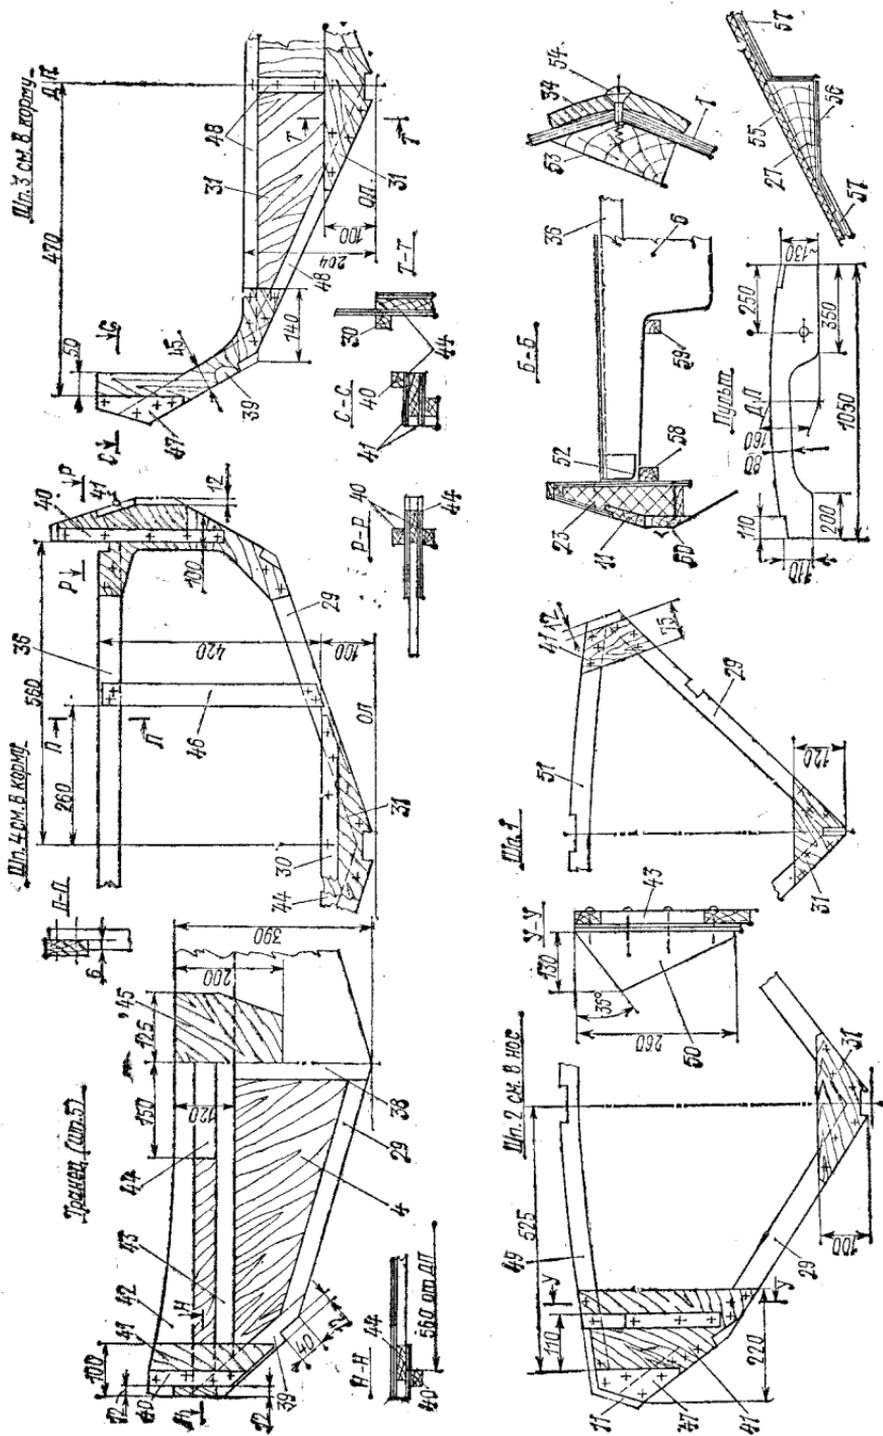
Шпангоутные рамы и узлы конструкции корпуса.
